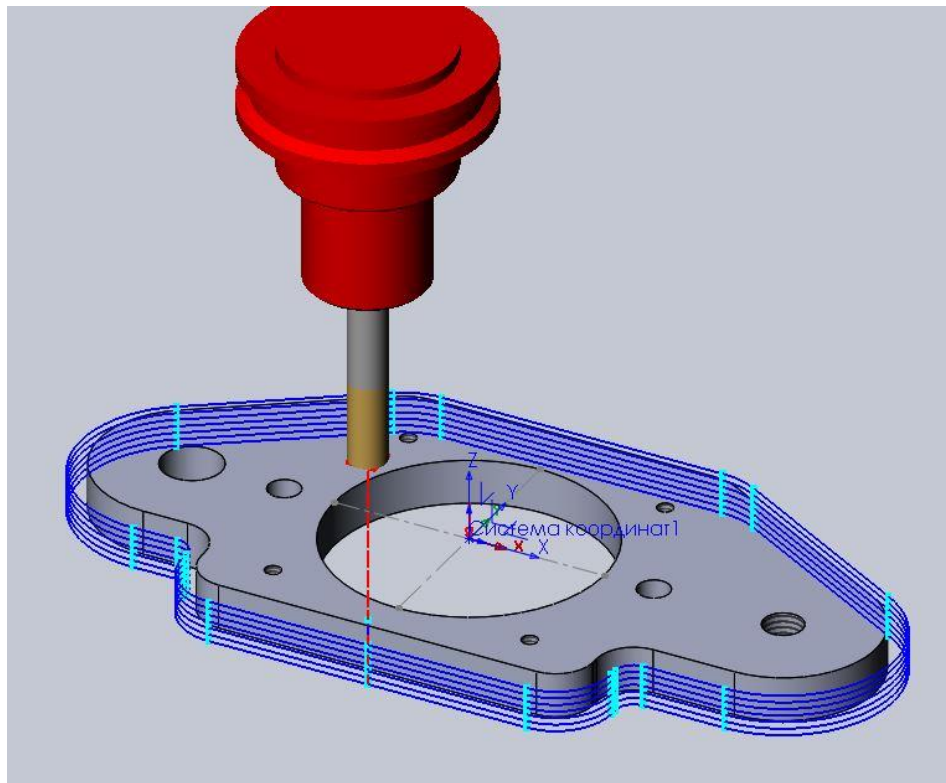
Фрезерування по зовнішньому контуру деталі
